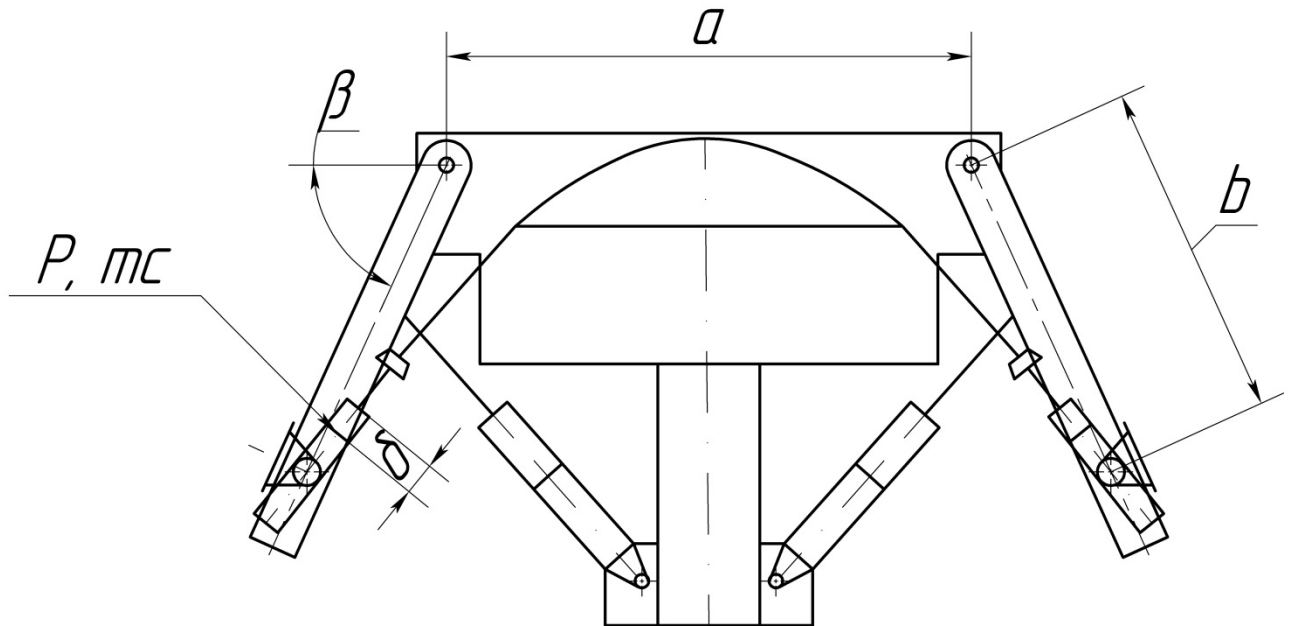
Основные силовые и кинематические ограничения гибочно-растяжных прессов
